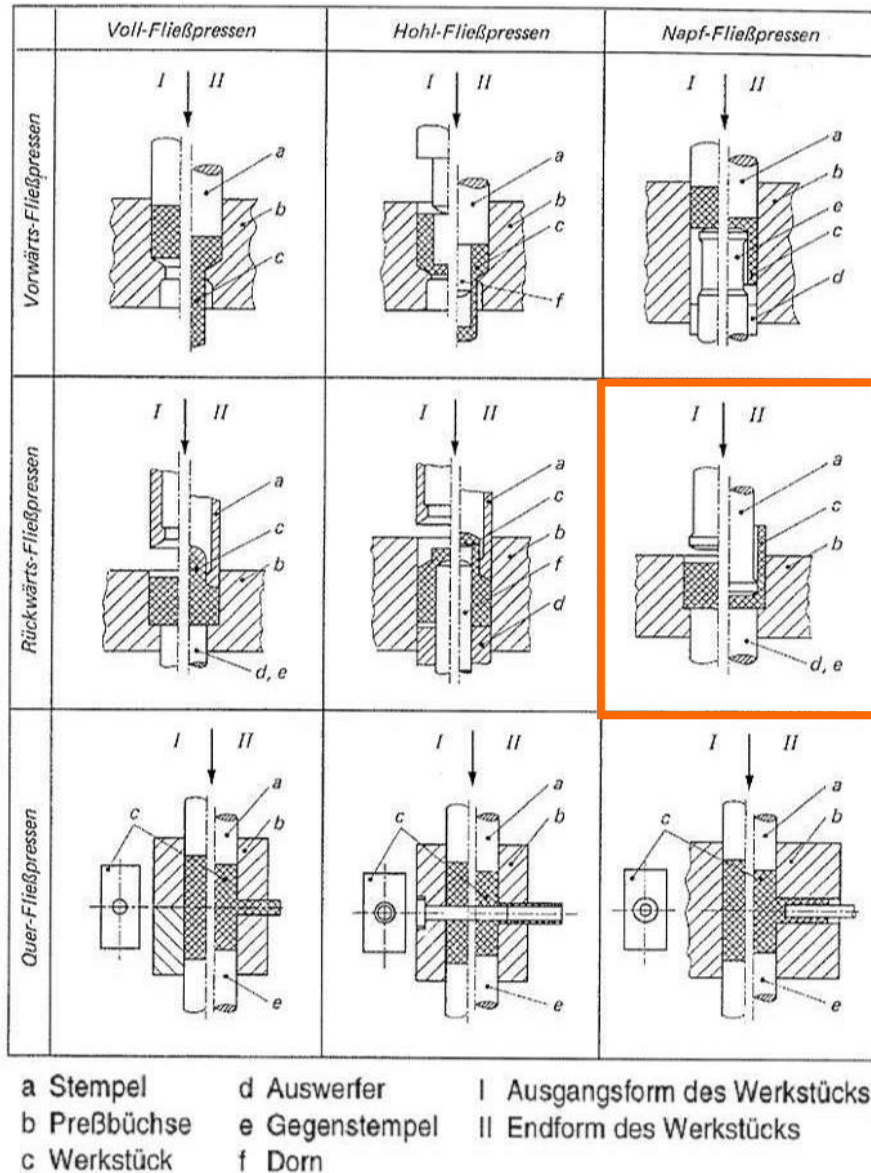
Werkzeugelemente und Grundverfahren des Fließpressens (DIN 8583-6) [29]
